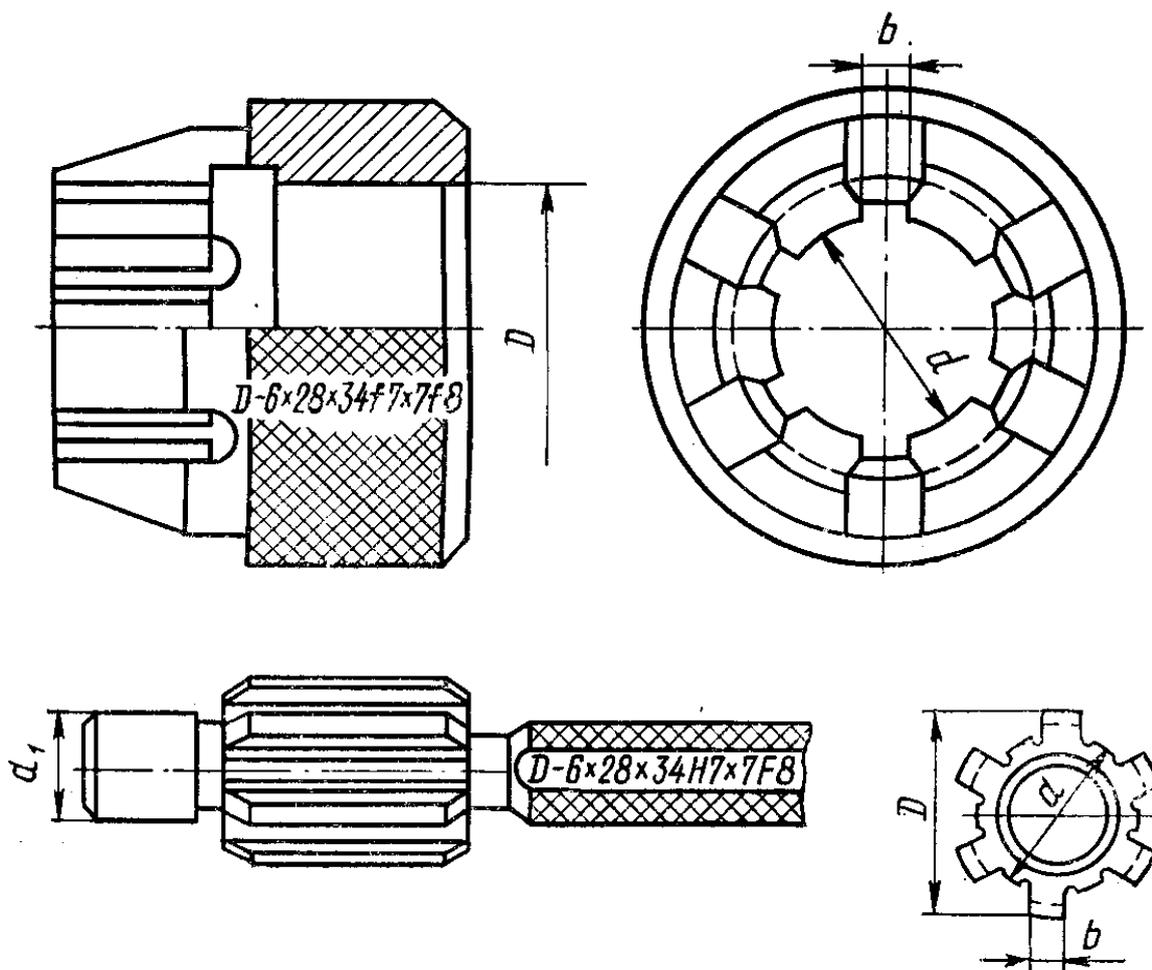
Комплексные калибры для контроля деталей шлицевых соединений
